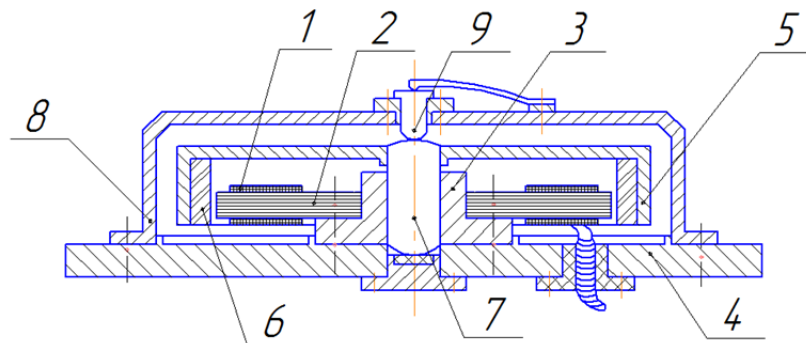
Конструкция предлагаемого микродвигателя-маховика
